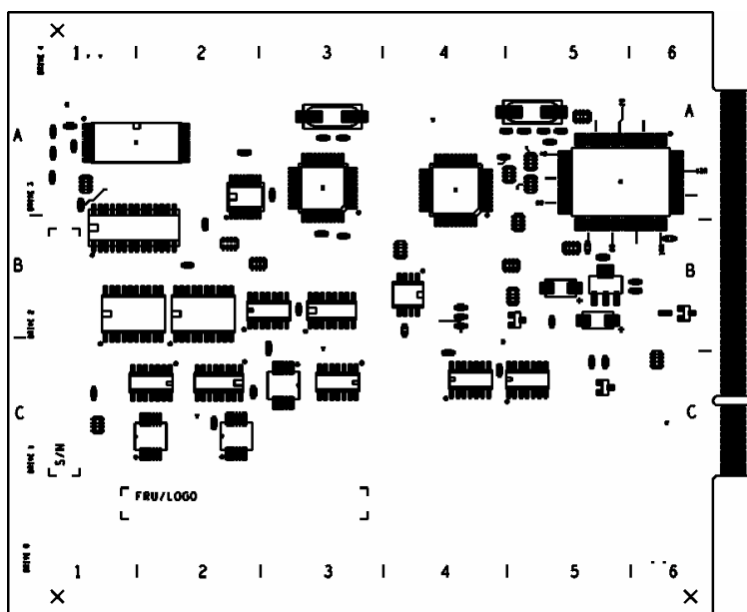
Объединительная плата для жестких дисков SAF-TE серверного корпуса SC5250-E
